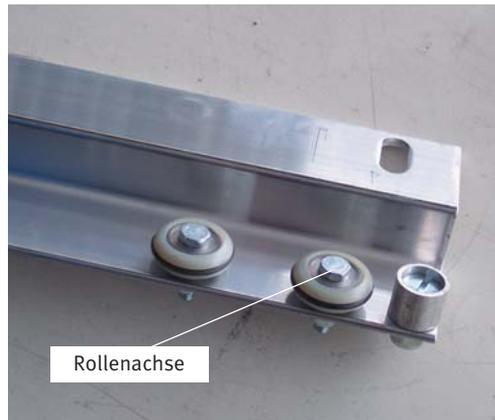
Schiebeaggregat mit Führungsrollen (Detailansicht)
